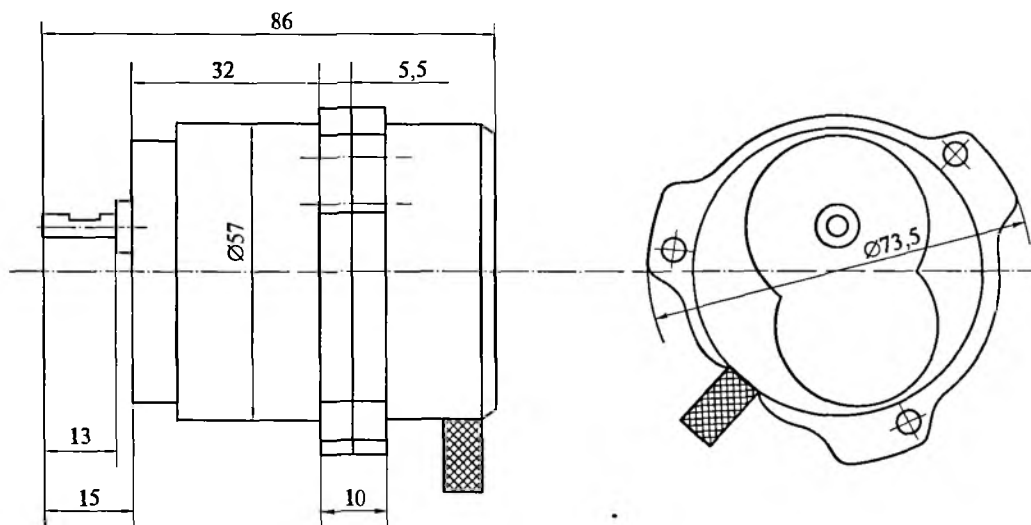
Габаритные и установочно-присоединительные размеры редукторного двигателя ДСР-2
